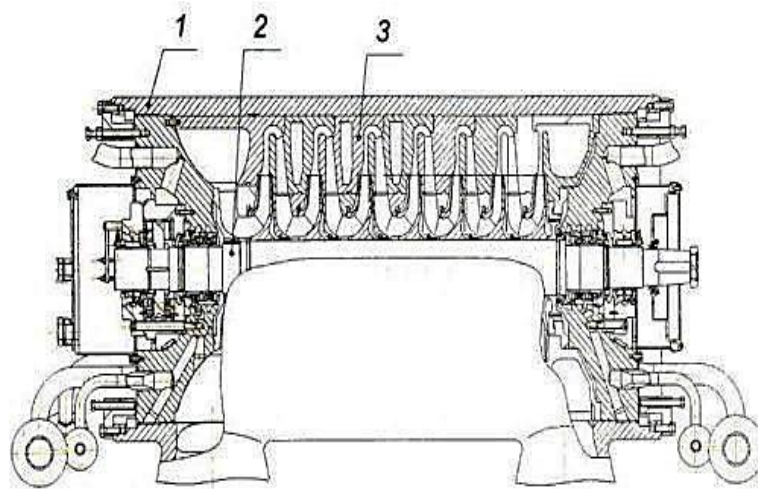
Базовий корпус з вертикальним роз'ємом
